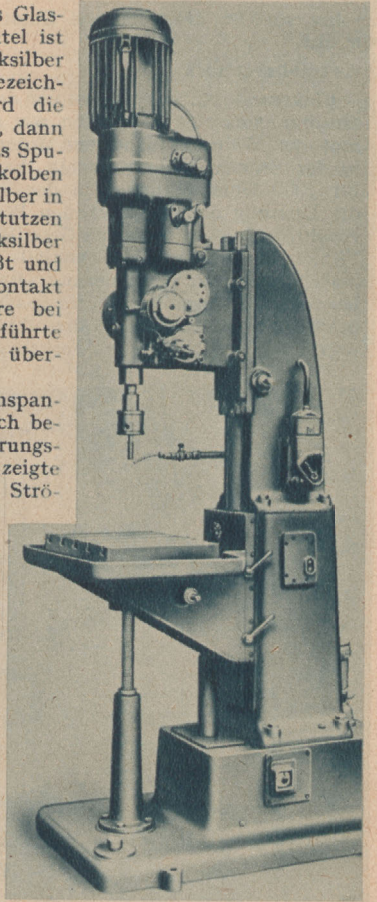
Drehstrommotor für 7000 Umdrehungen in der Stunde an einer Gewindeschneidmaschine
